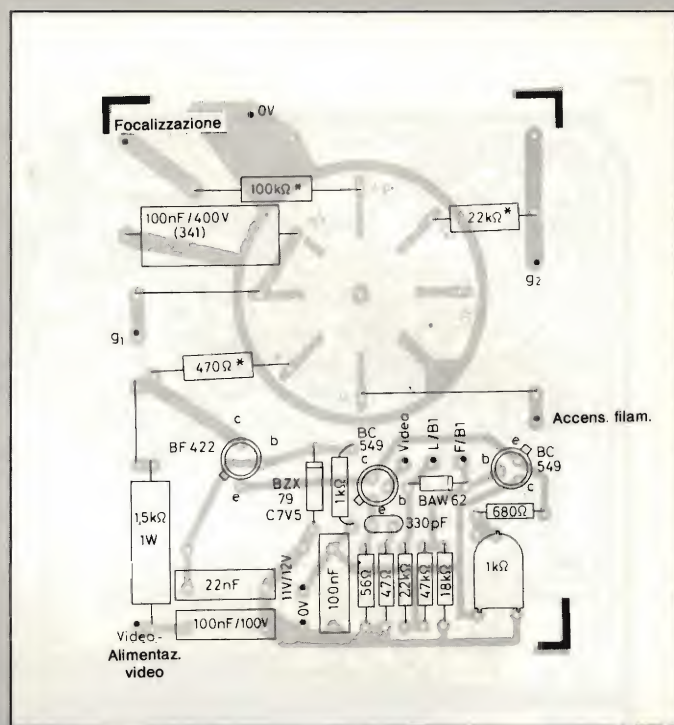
Piastra del circuito stampato di figura 8 con i componenti montati.
